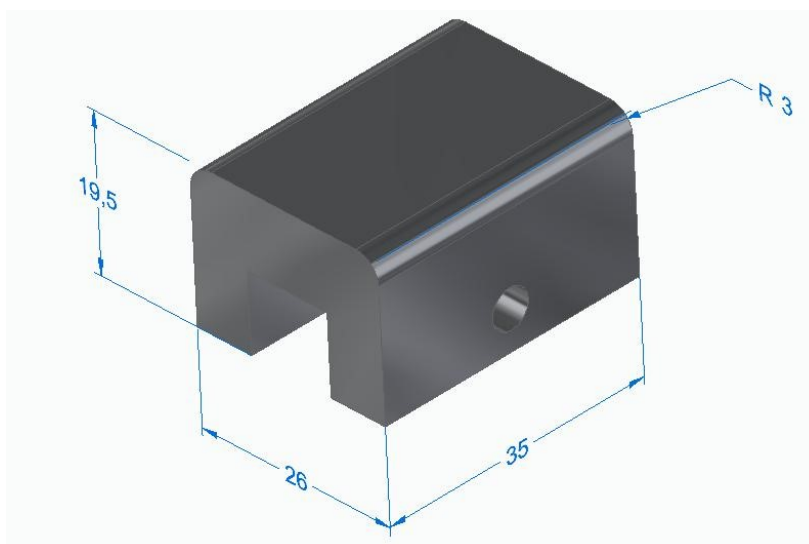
Desenho esquemático do dispositivo utilizado na execução dos ensaios SDT.
